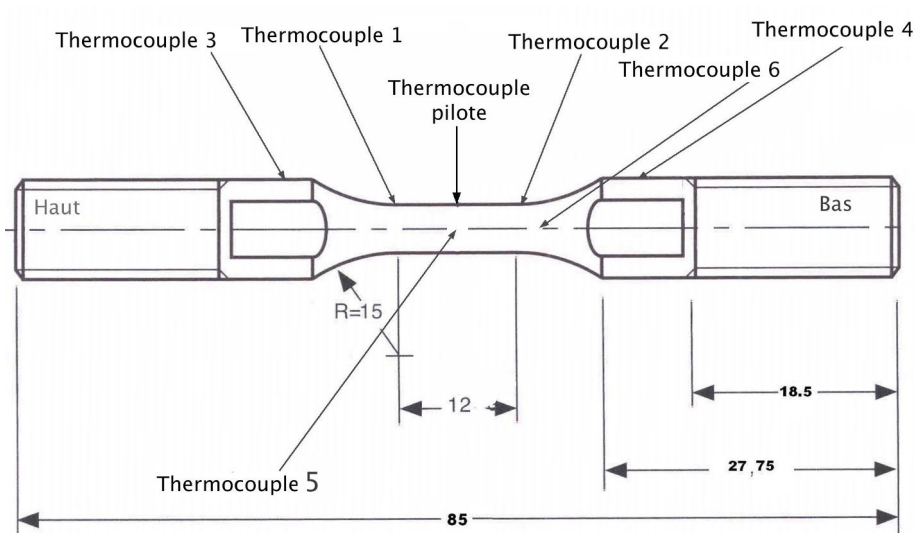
Emplacement des thermocouples pour l'éprouvette de géométrie cylindrique
